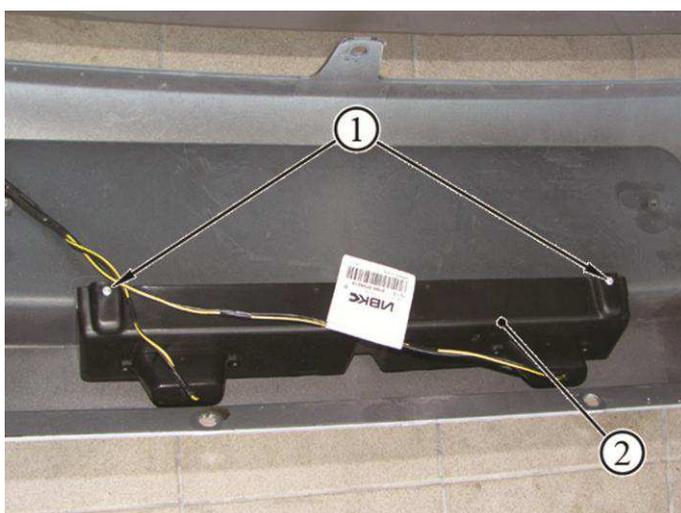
Кронштейн крепления фонаря освещения номерного знака:
